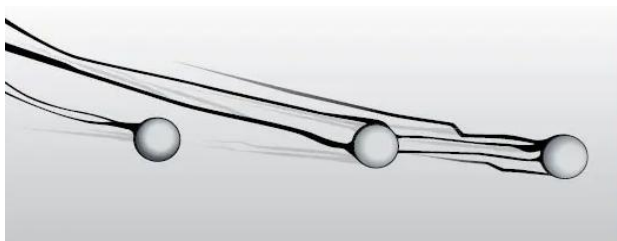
Продукти фретинг-корозії на поверхні обшивки поблизу заклепок [32].
